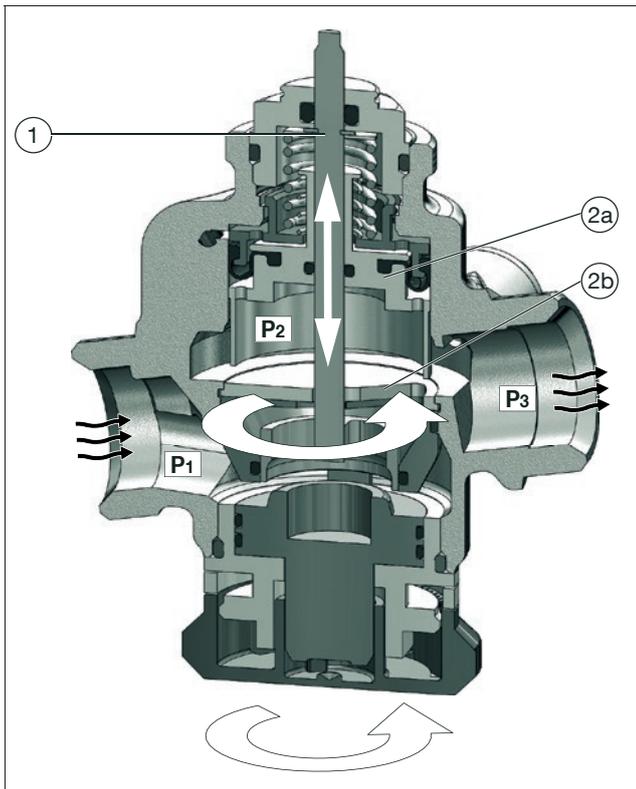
Vue en coupe du régulateur « Cocon QDP »
